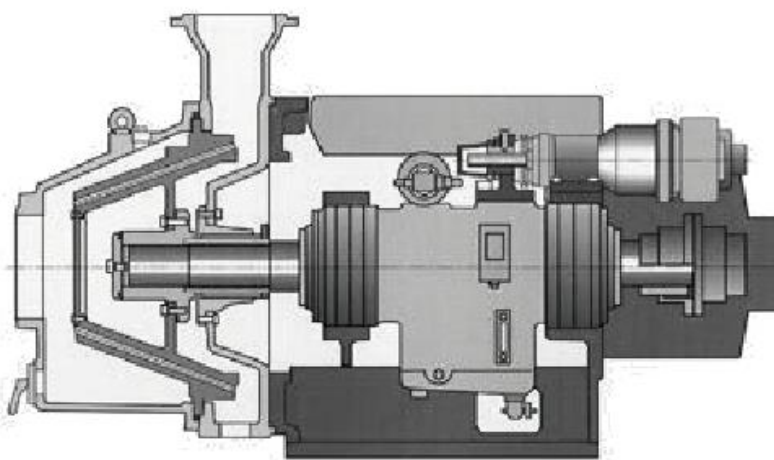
Uproszczony schemat budowy holendra [212]
